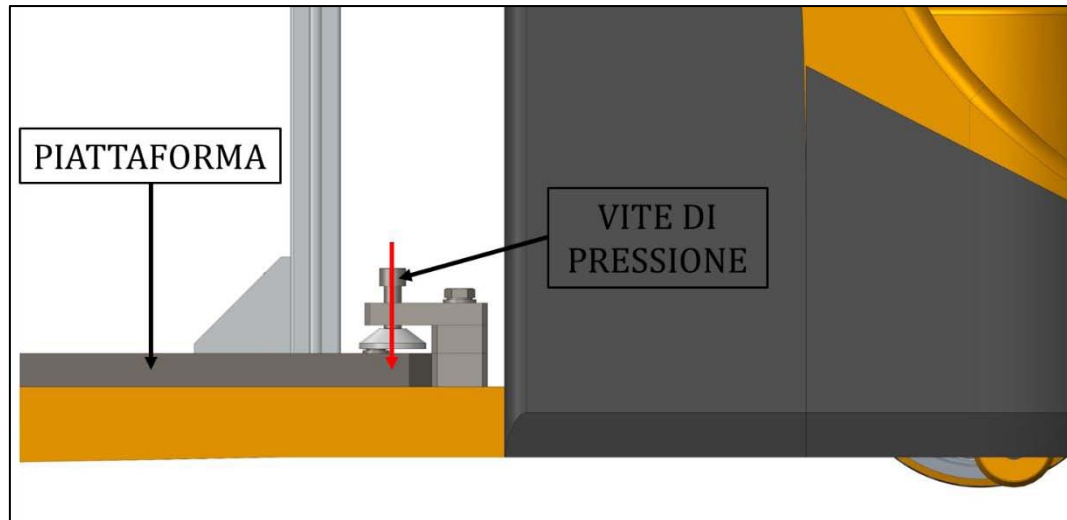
Centraggio delle forche del transpallet rispetto la piattaforma del sistema di estrazione.
